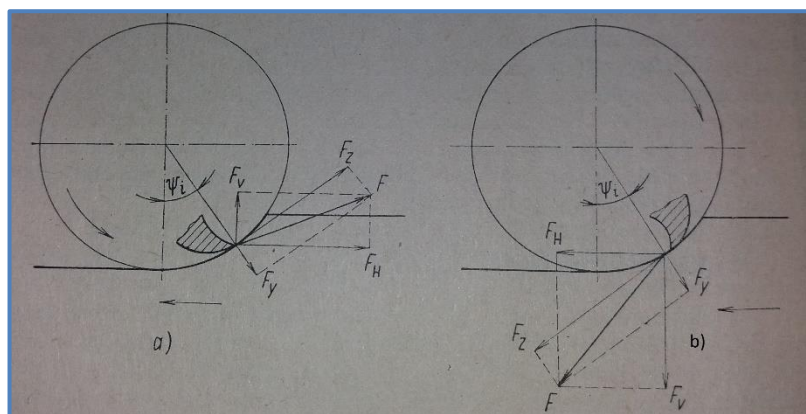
Rozklad celkové řezné síly na zubu nástroje při rovinném frézování válcovou frézou s přímými zuby. Legenda: D – hlavní bod ostří; F_a – aktivní síla; F_c – řezná síla; F_e – pracovní síla; F_{eN} – kolmá pracovní síla; F_f – posuvová síla; F_{fN} – kolmá síla posuvu; φ – úhel posuvového pohybu; η – úhel řezného pohybu [3].
